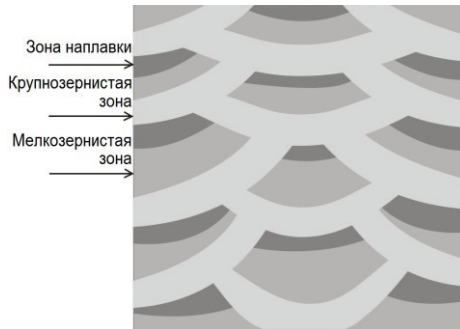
Представительный объем многопроходного сварного шва
